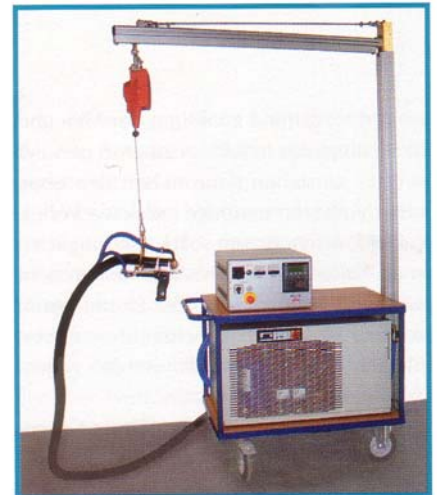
Mobile Lötanlage, bestehend aus MF-Generator Typ MFG 15 mit Lötpestole, Balancer-aufhängung und Kühlgerät.
